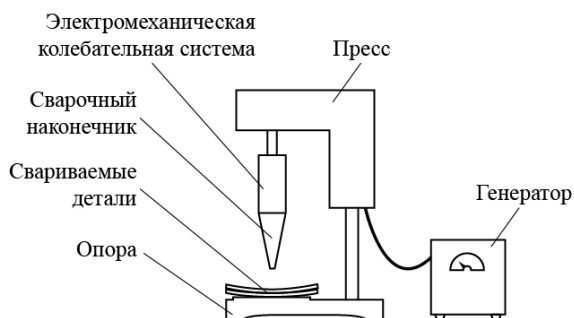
Схема установки для ультразвуковой сварки термопластичных полимерных материалов
